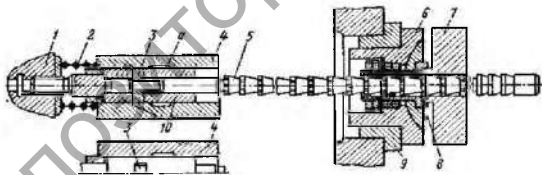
Схема крепления инструмента и детали на протяжной операции
